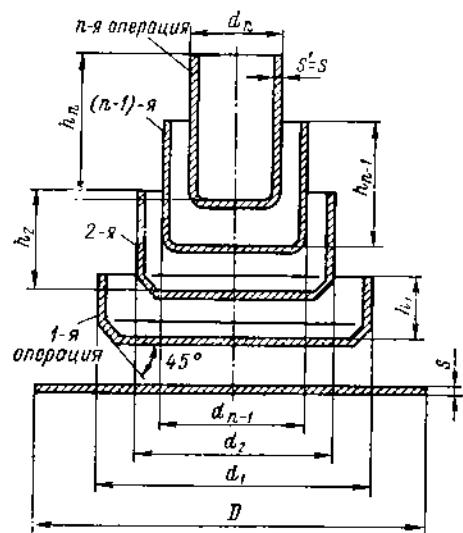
Схема получения полого изделия диаметром d_n и высотой h_n из плоской заготовки D
